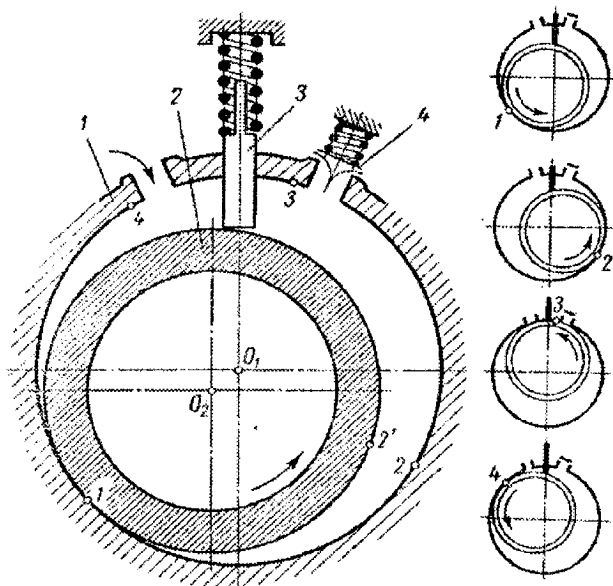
Схематичний розріз ротaційного компресора з ротором, що котиться. 1 – циліндр; 2 – ротор; 3 – пластина; 4 – нагнітальний клапан.
